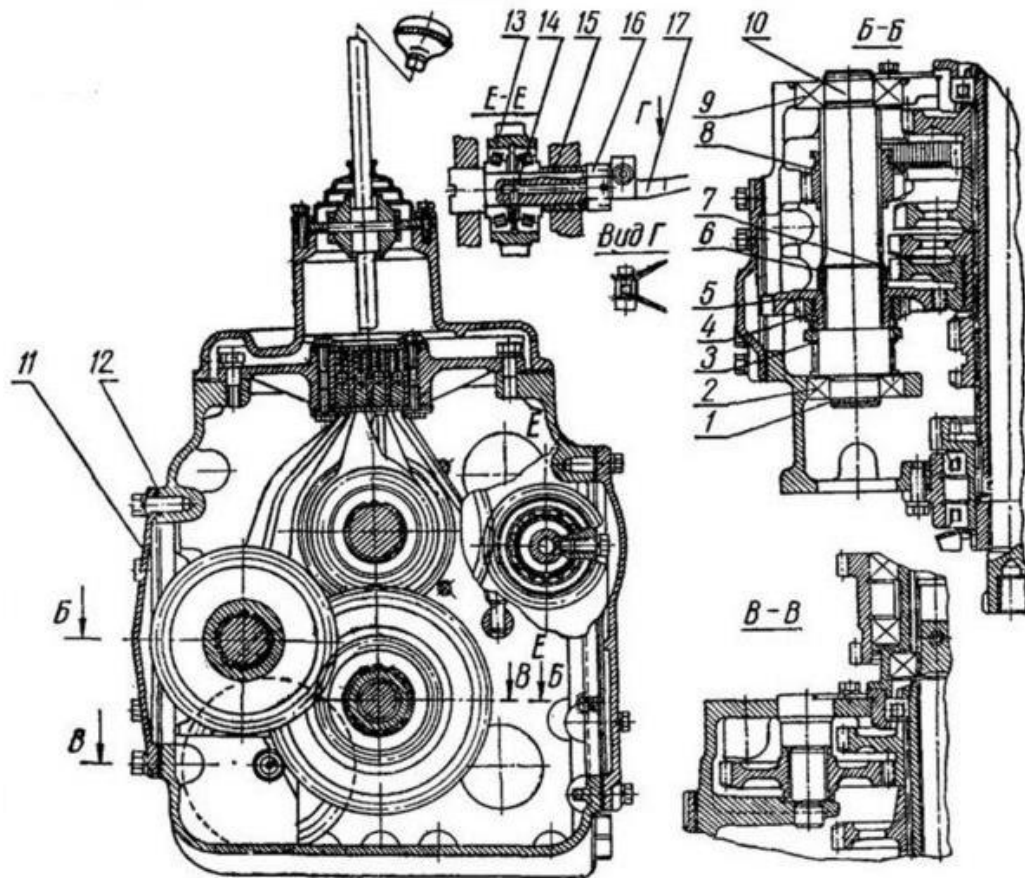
Коробка перемини передач МТЗ (поперечний розріз): 1– кільце стопорне; 2–підшипник ШРО-208; 3–кільце пружинне; 4–шестерня ведуча включення ходозменшувача; 5–шестерня ведуча I передачі і заднього ходу; 6–шайба упорна; 7–кільце штопорне; 8–шестерня ковзна I передачі і заднього ходу; 9–підшипник ШРО-50308; 10–вал першої передачі і заднього ходу; 11–ліва кришка бокового лючка; 12–прокладка кришки бокового лючка; 13–шестерня проміжна приводу переднього ведучого моста; 14–вісь проміжної шестерні; 15–втулка; 16–гайка; 17–лоток.
